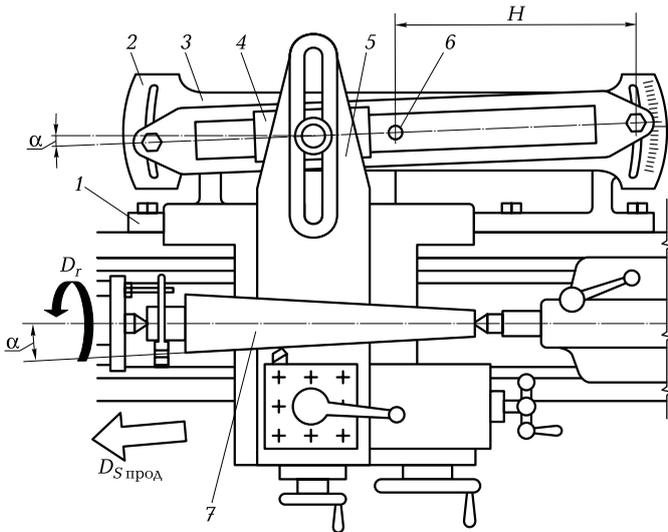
Обработка конической поверхности с помощью копировальной (конусной) линейки:
